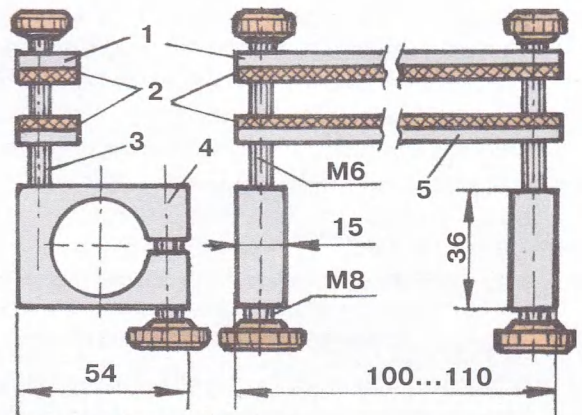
Кронштейн крепления ручки дрели: 1 – пластина верхняя; 2 – резина; 3 – винт-фиксатор (длина 45 мм); 4 – сухарь (2 шт.); 5 – пластина нижняя.
